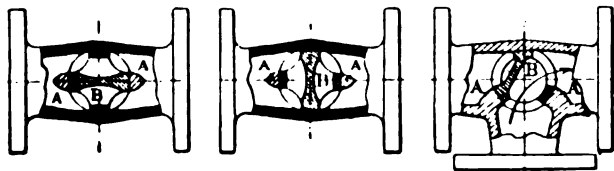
, 18 e 19. — Rubinetti speciali per liquidi corrosivi.
